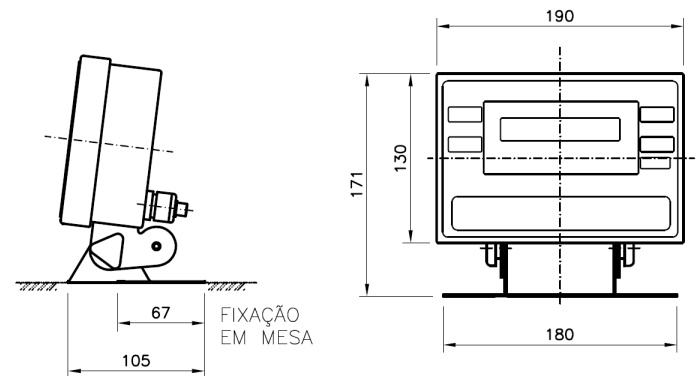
Linha 3100C detalhe fixação em Mesa e dimensões
